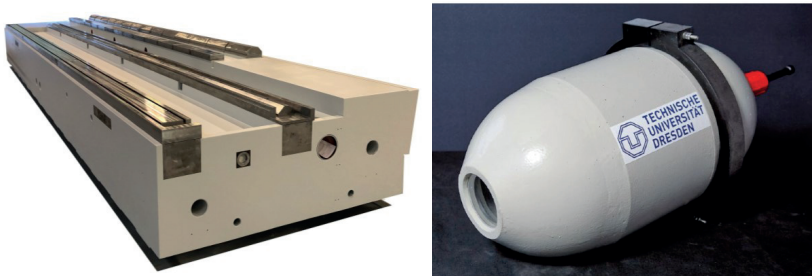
Links: Maschinenbett für eine Walzenschleifmaschine GEORG ultragrind SG 2 der Heinrich Georg GmbH Maschinenfabrik [47] (Foto: durcrete GmbH); rechts: UHPC-Druckgehäuse mit Beschichtungssystem [46]
